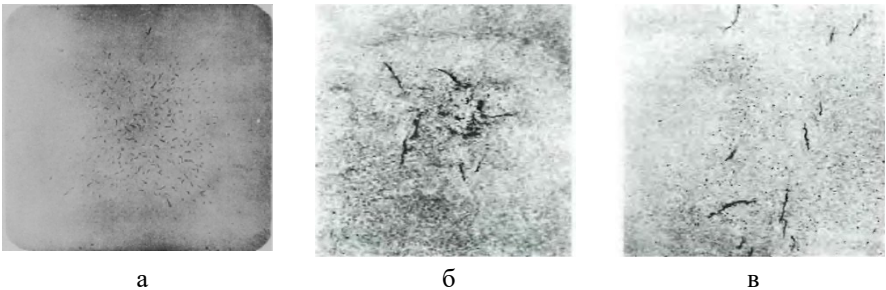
Флокени в поперечному перерізі литої заготовки (а) і готовому прокаті (б, в)
